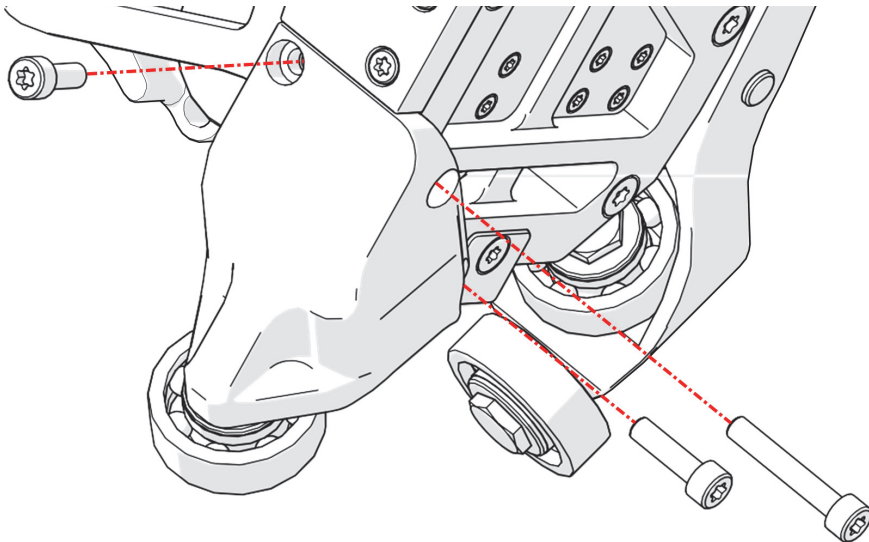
Extracción de los tornillos del ensamblaje rueda-cojinete
